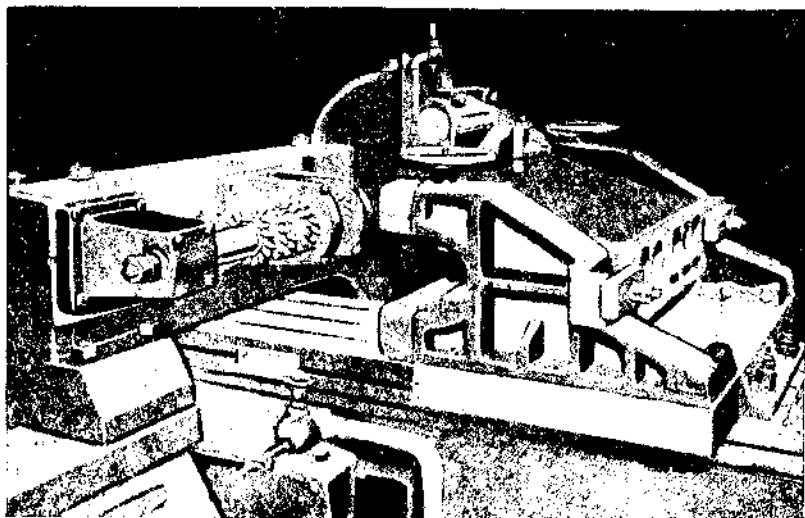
Фрезеровка торцов гнезда подшипников коленчатого вала.
